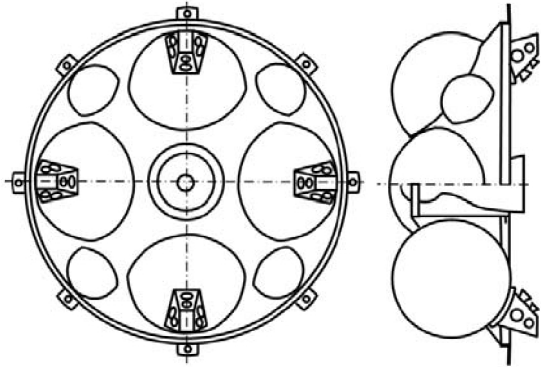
Компонировочная схема комплексной двигательной установки с передачей усилия на нижнюю часть приборно-агрегатного отсека
